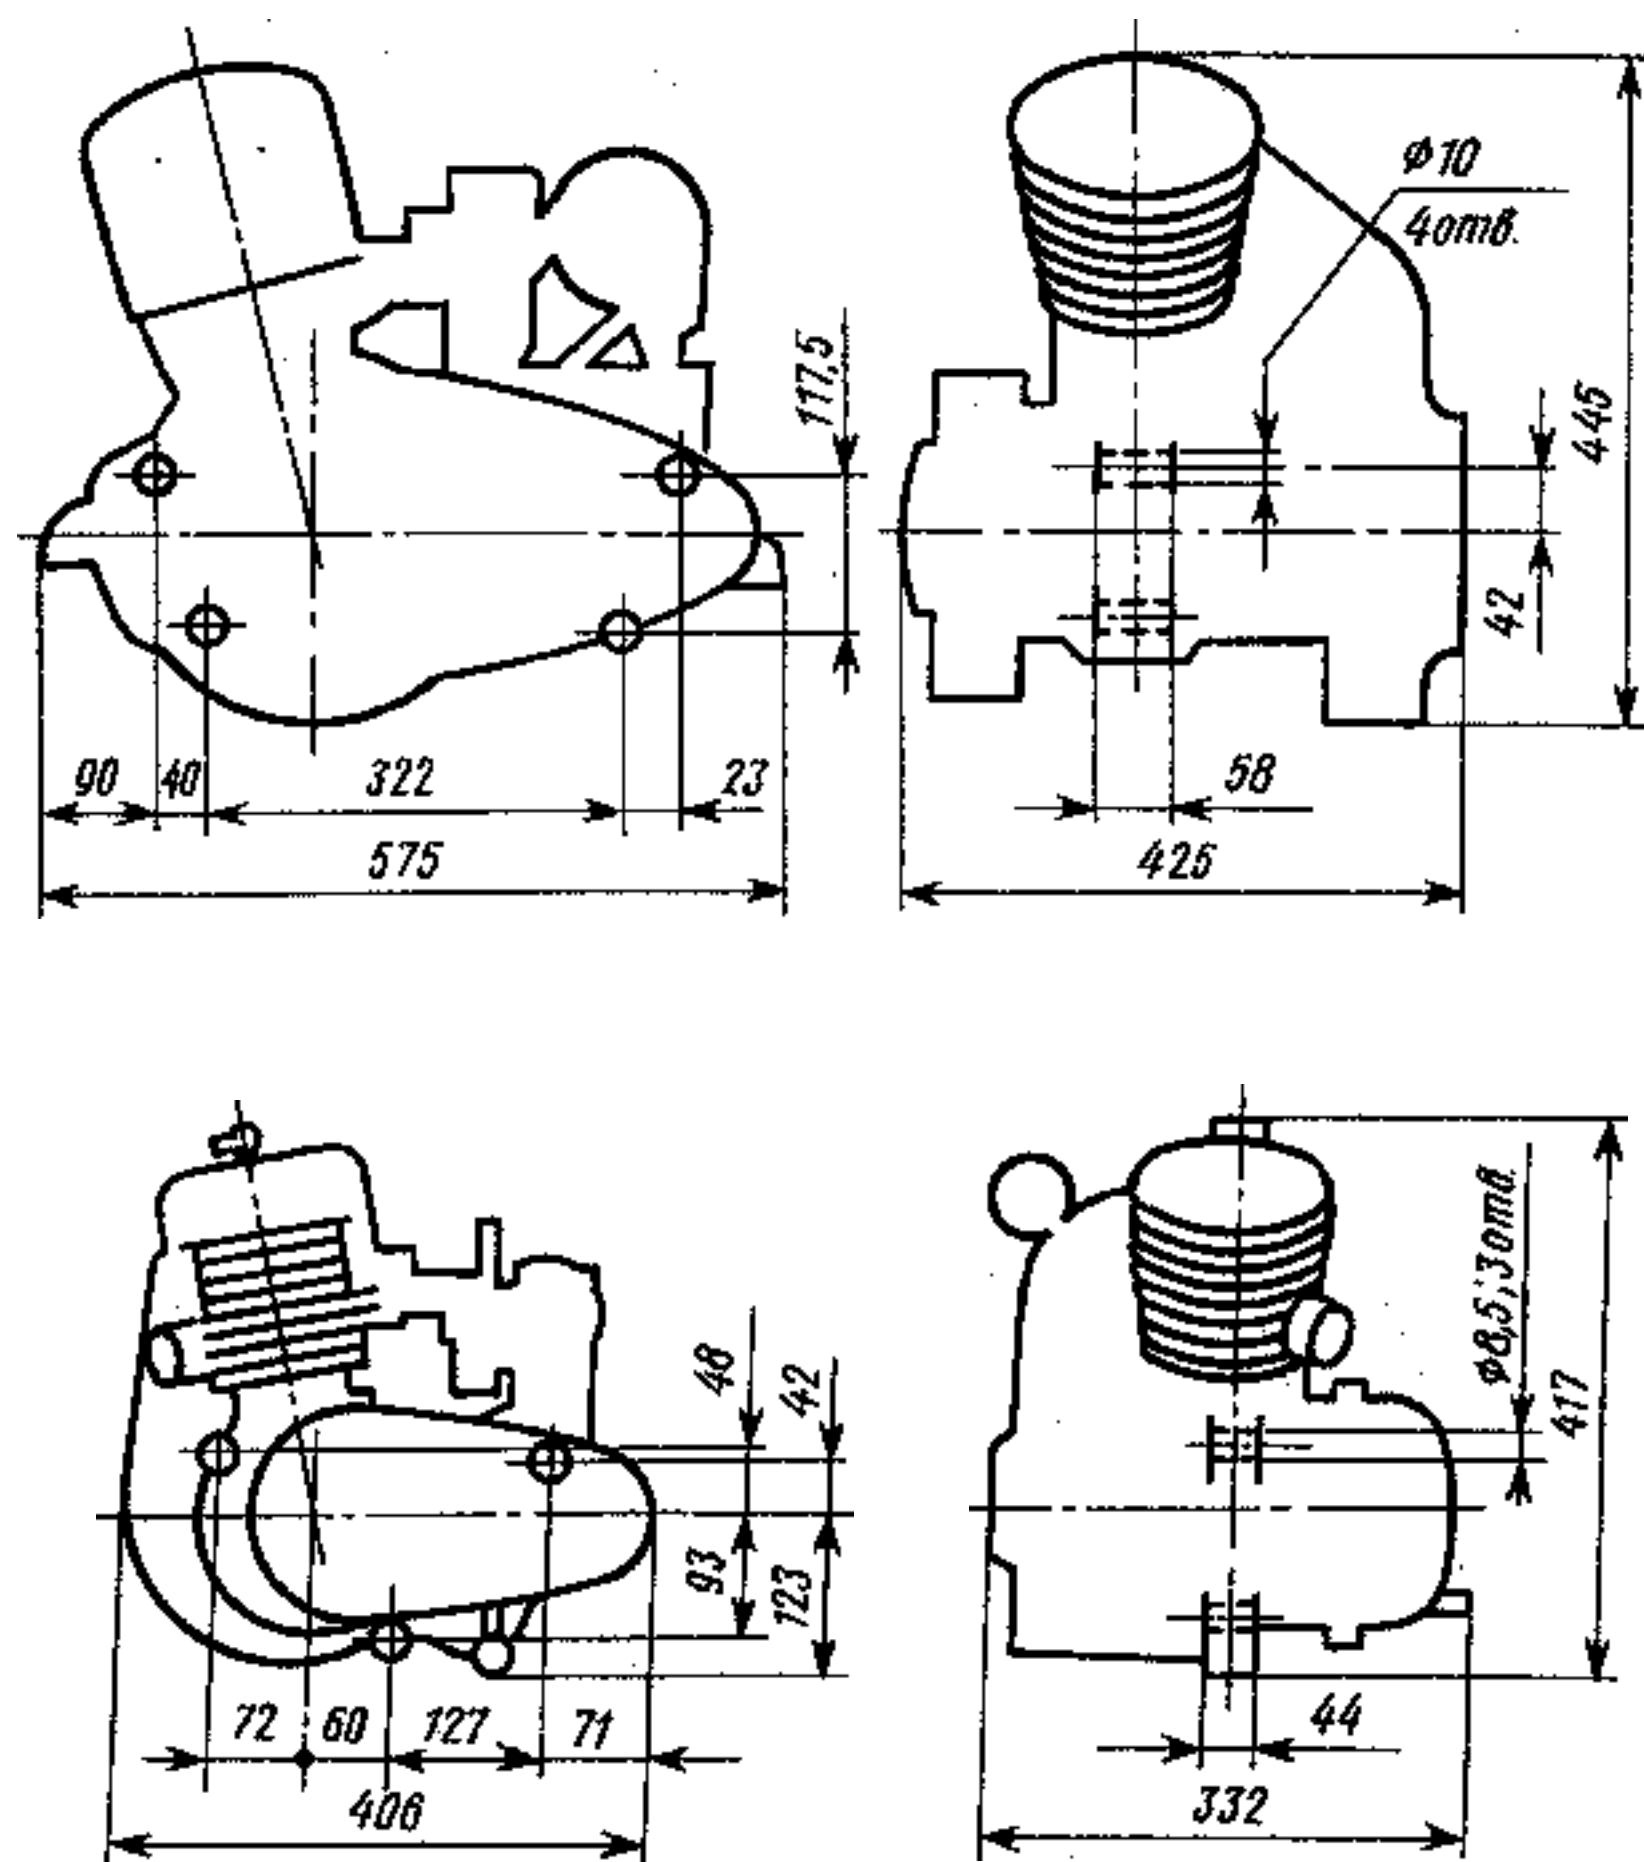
Габариты и точки крепления двигателей СМЗ и ТГ-200
